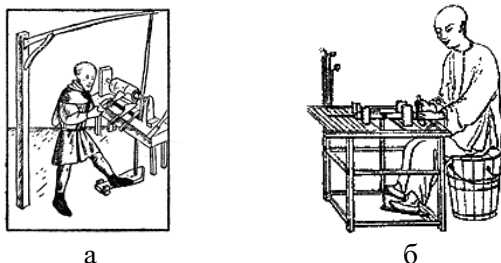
Токарні пристрої з ножним "приводом"
